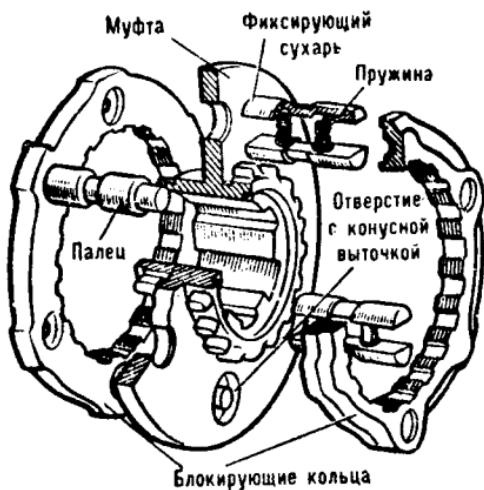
Синхронизатор коробки передач автомобиля ЗИЛ-130
